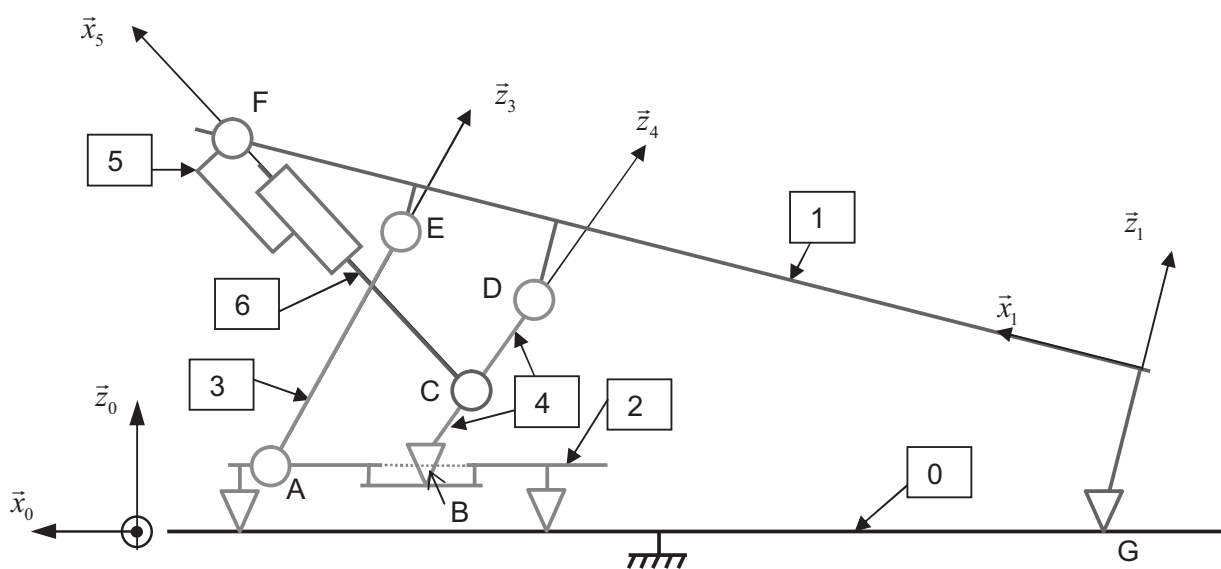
Schéma cinématique plan du dispositif d'inclinaison
